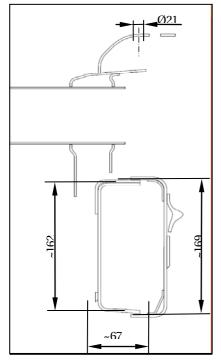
Sección Q-Q (Amarok SC)
